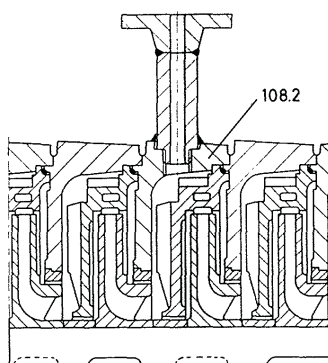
Corpo de estágio com derivação roscada e soldada
